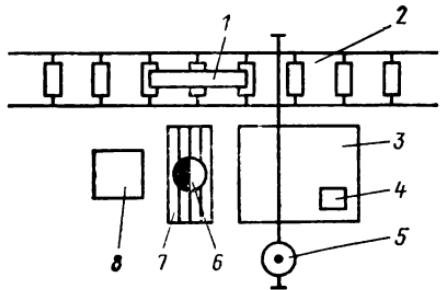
Рабочее место контролера, проверяющего отливки массой более 20 кг:
